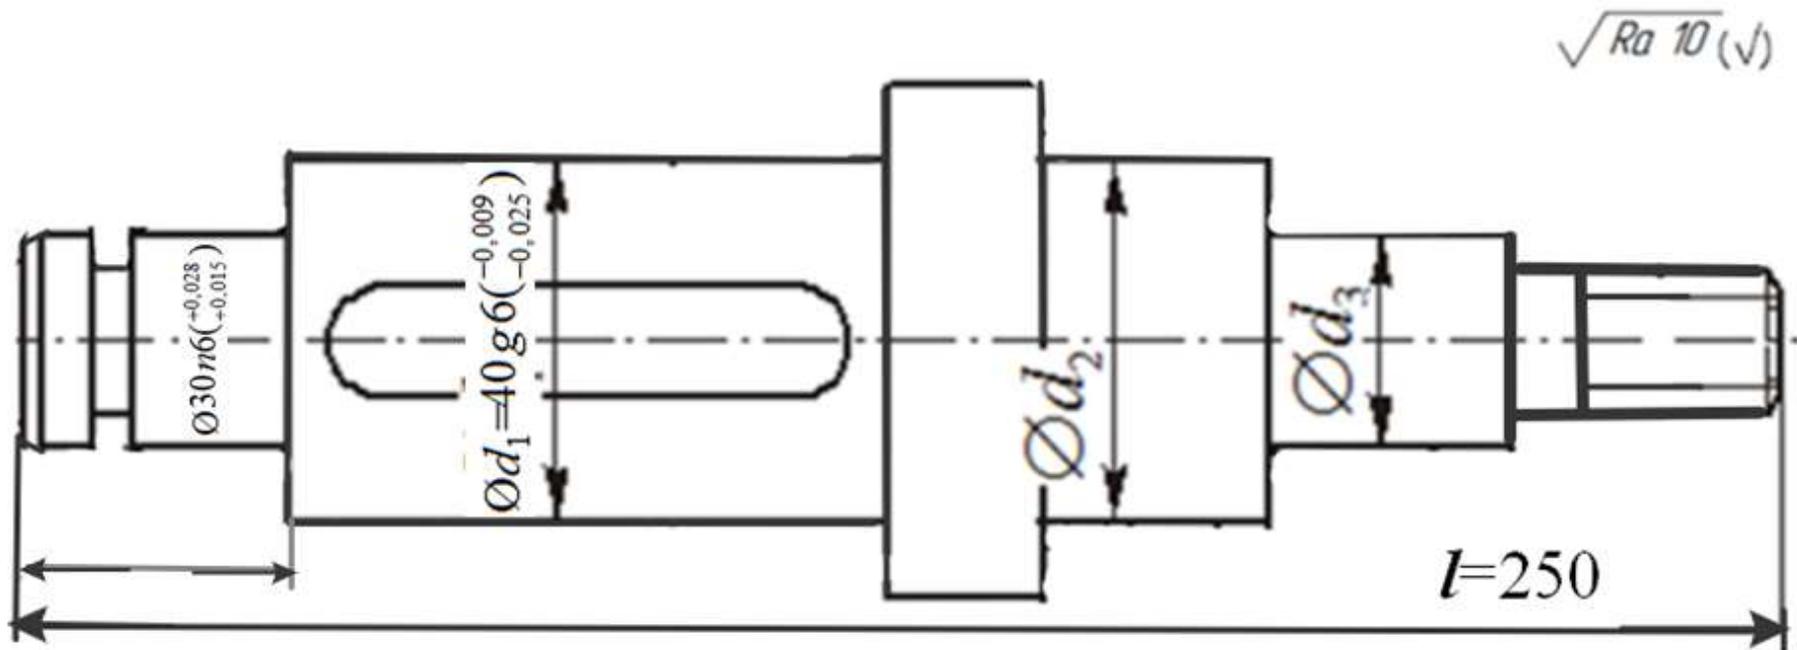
Пример эскиза вала (начало простановки исполнительных размеров и пр.) из сборочного эскиза редуктора
